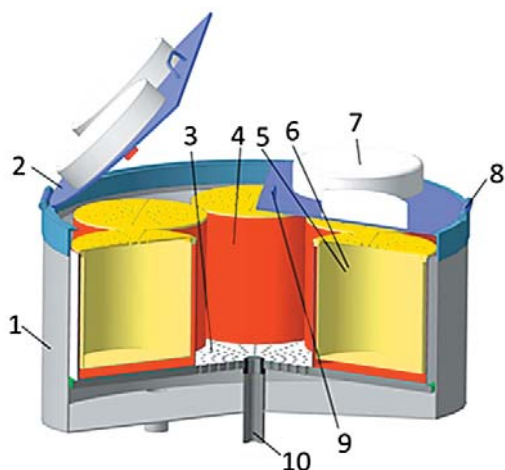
Установка с передвижными цилиндрическими резонаторами
